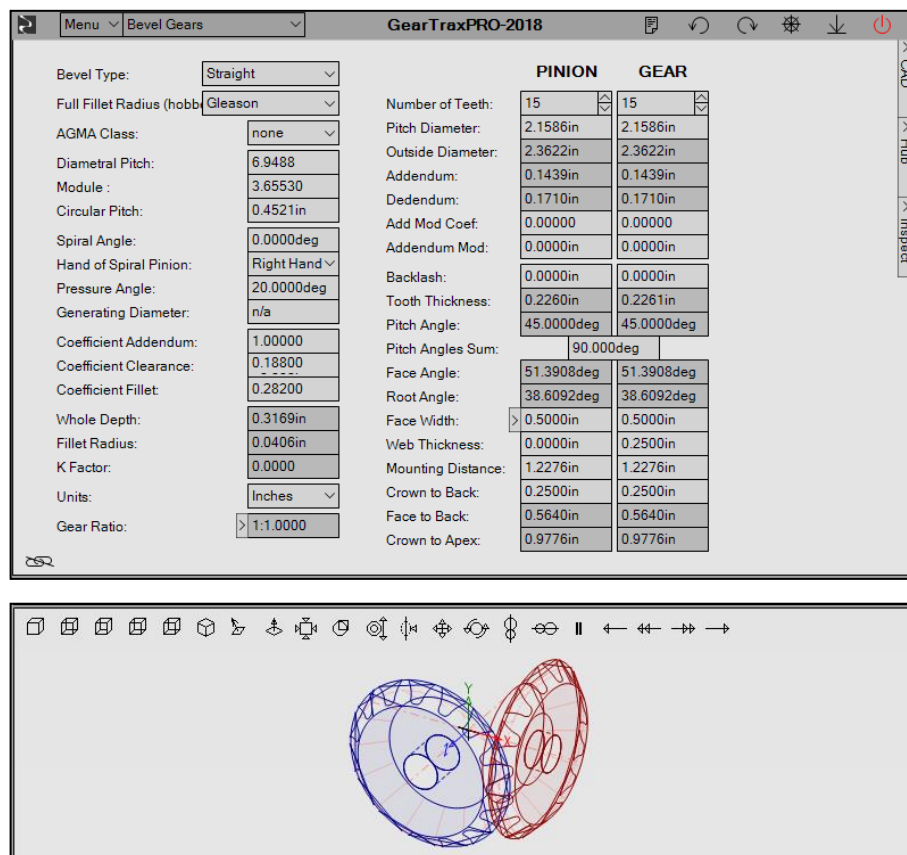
Piñón cónico del eje principal en Gear Trax
